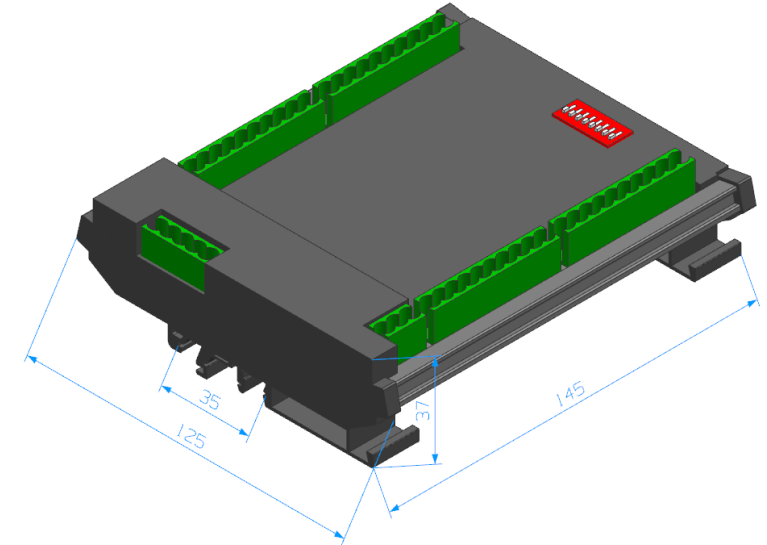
ZIO1616MT 安装尺寸图 (单位: mm)
